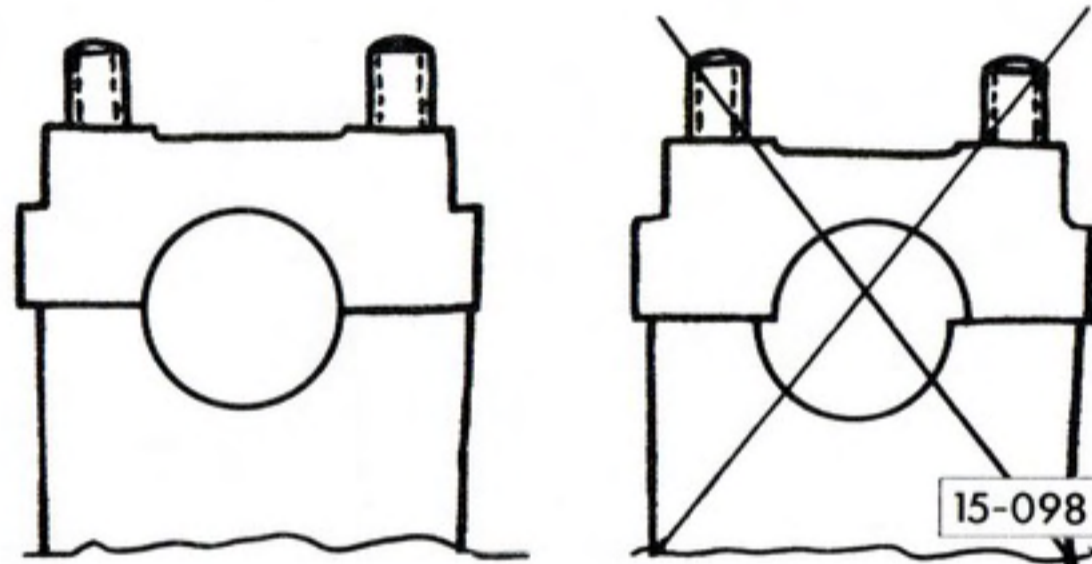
Einbaulage Lagerdeckel-Nockenwelle
